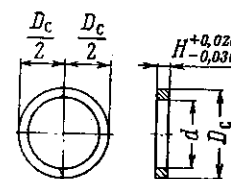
Типовая конструкция полуколец для механического осаживания защитных фторопластовых шайб
